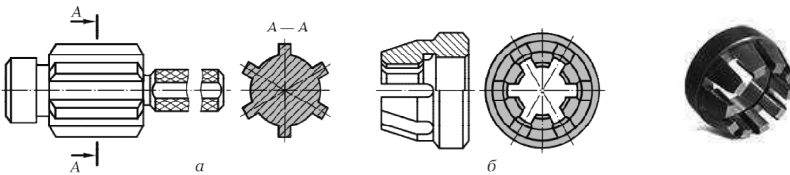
Калібри для контролю деталей шліцевого з'єднання:
